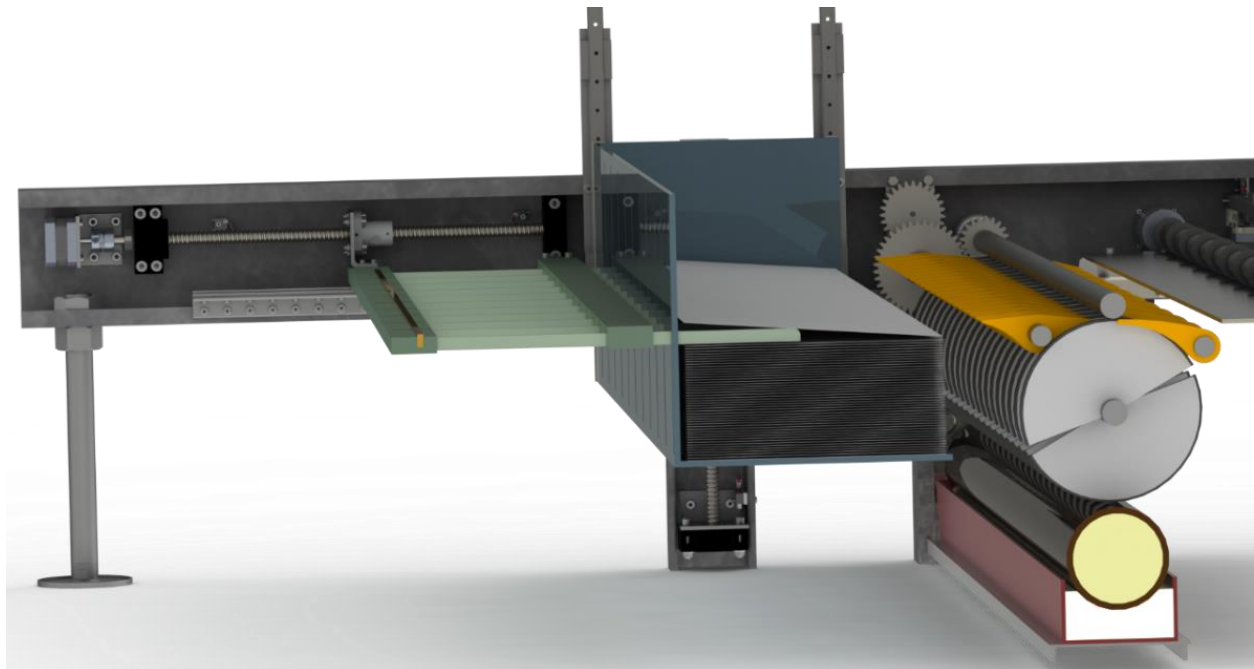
Las uñas alcanzan el final de carrera y están listas para recibir la plancha de papel
